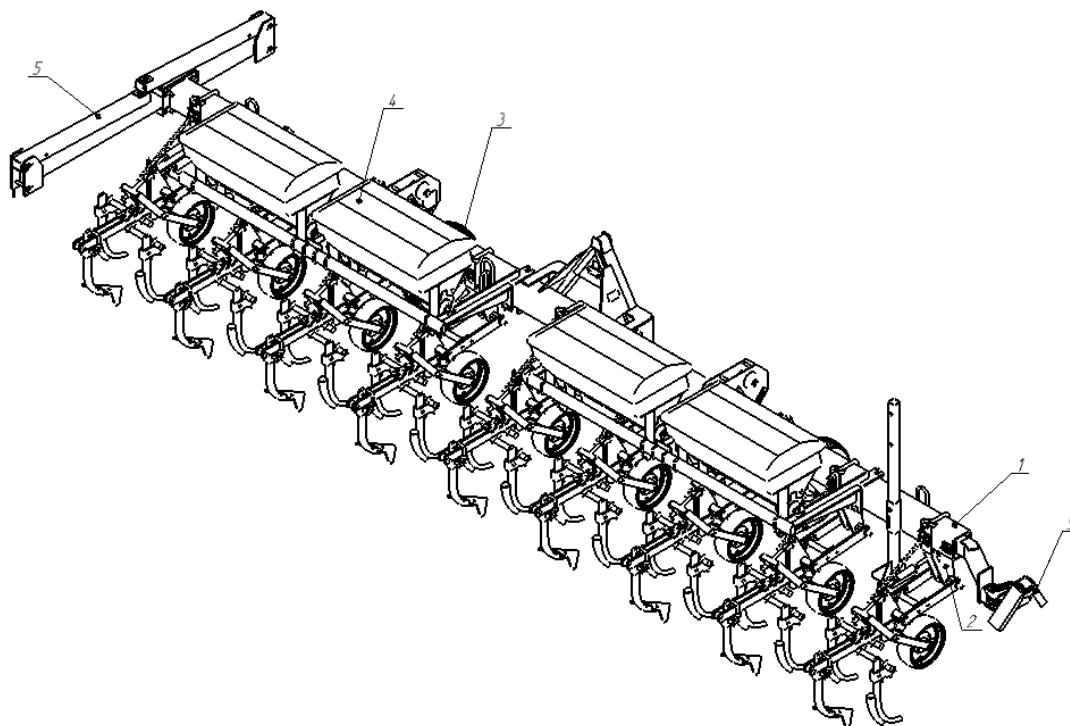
Общий вид культиватора КПМ-5,6ТП-01
